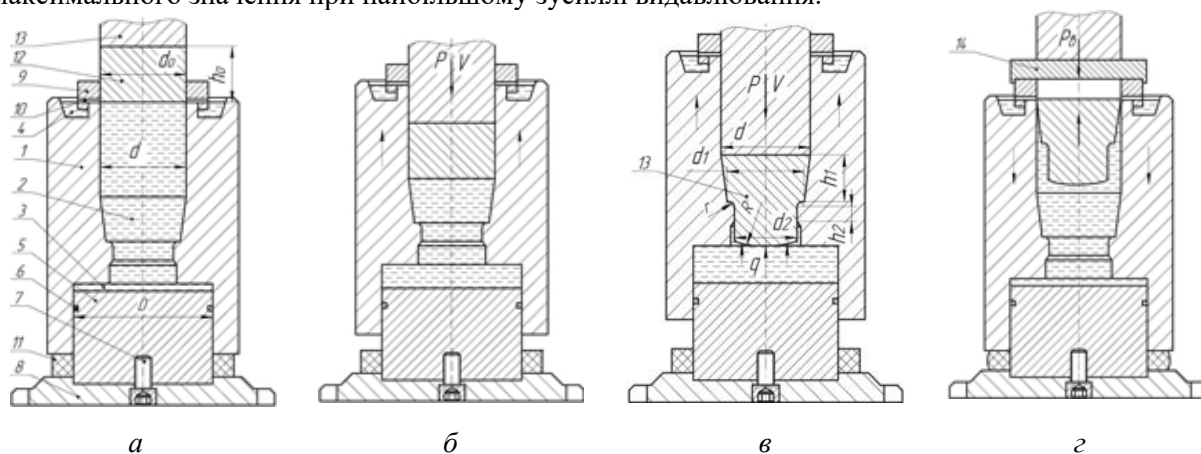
Положення інструмента і заготовки на різних етапах видавлювання: а – положення у вихідному стані (1 – контейнер, 2 – верхня камера, 3 – нижня камера, 4 – резервуар для рідини, 5 – плунжер, 6 – ущільнення, 7 – гвинт, 8 – нижня плита, 9 – кільце, 10 – отвір, 11 – кільце із поліуретану, 12 – заготовка, 13 – пуансон), б – положення на початку видавлювання, в – положення в кінці видавлювання з позначенням розмірів деформованої заготовки, г – положення в кінці виштовхування деформованої заготовки (14 – плита)
